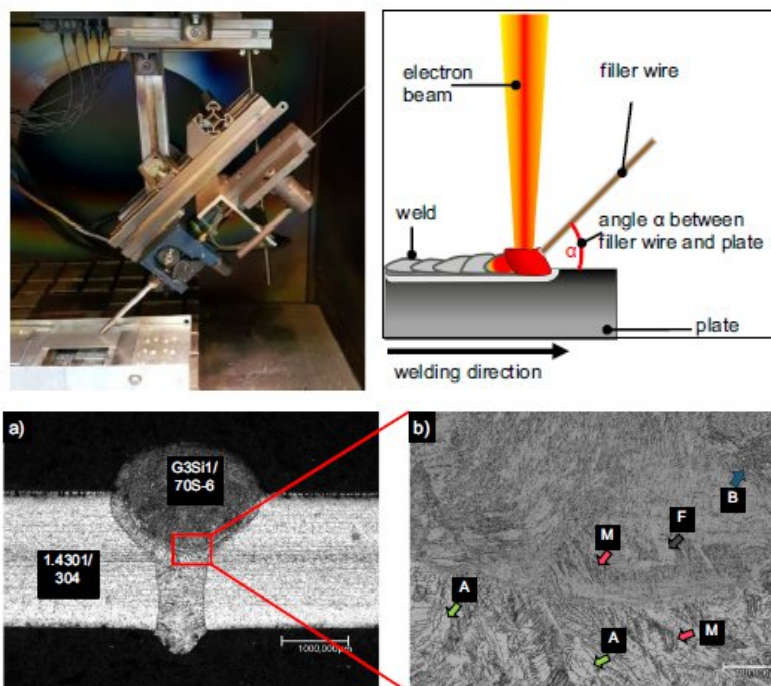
Elektronenstrahl Schweißaufbau und Makro- sowie Mikroschliffe der Schweißnaht
